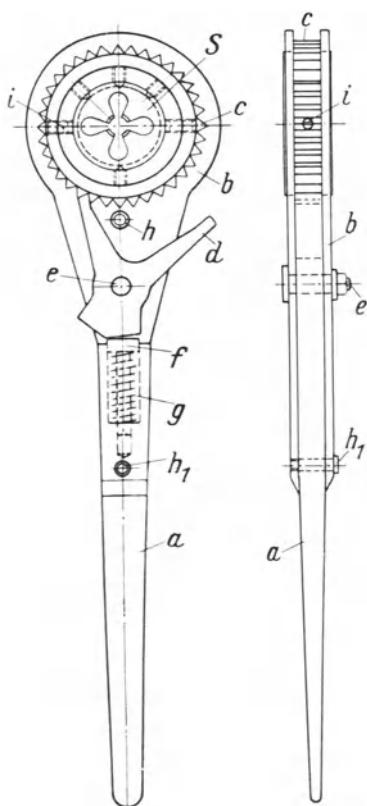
Hand-Gewindeschneidkluppe für eingemauerte Sockelschrauben.
